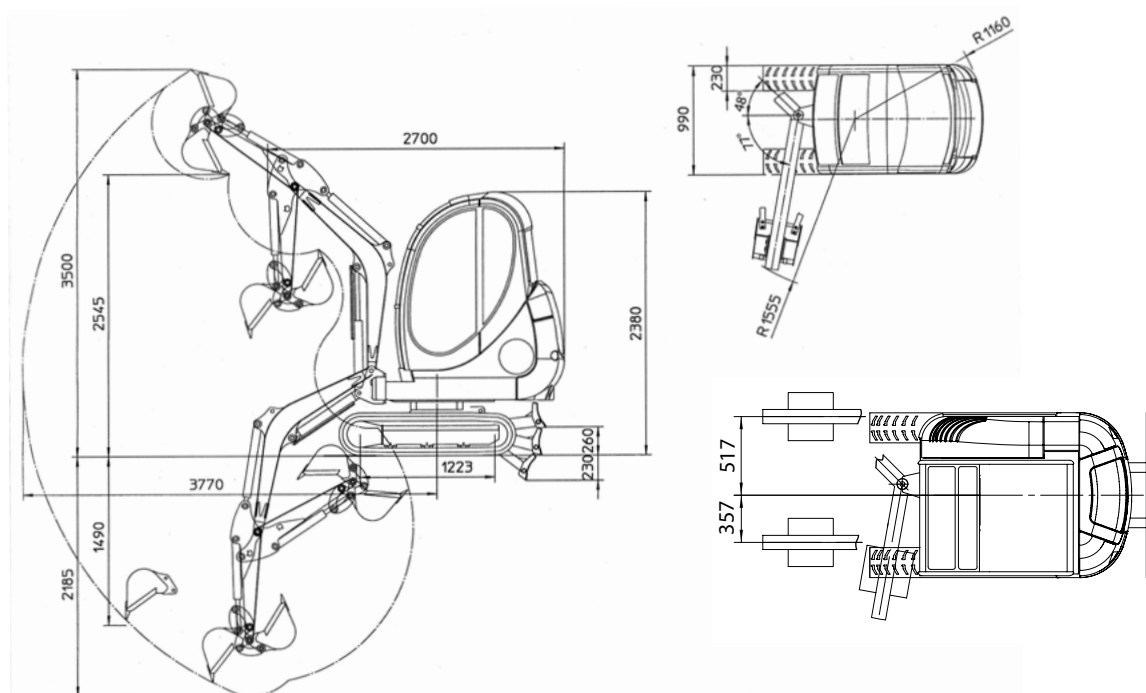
Køretøjets dimensioner (type 1703 VDS)
